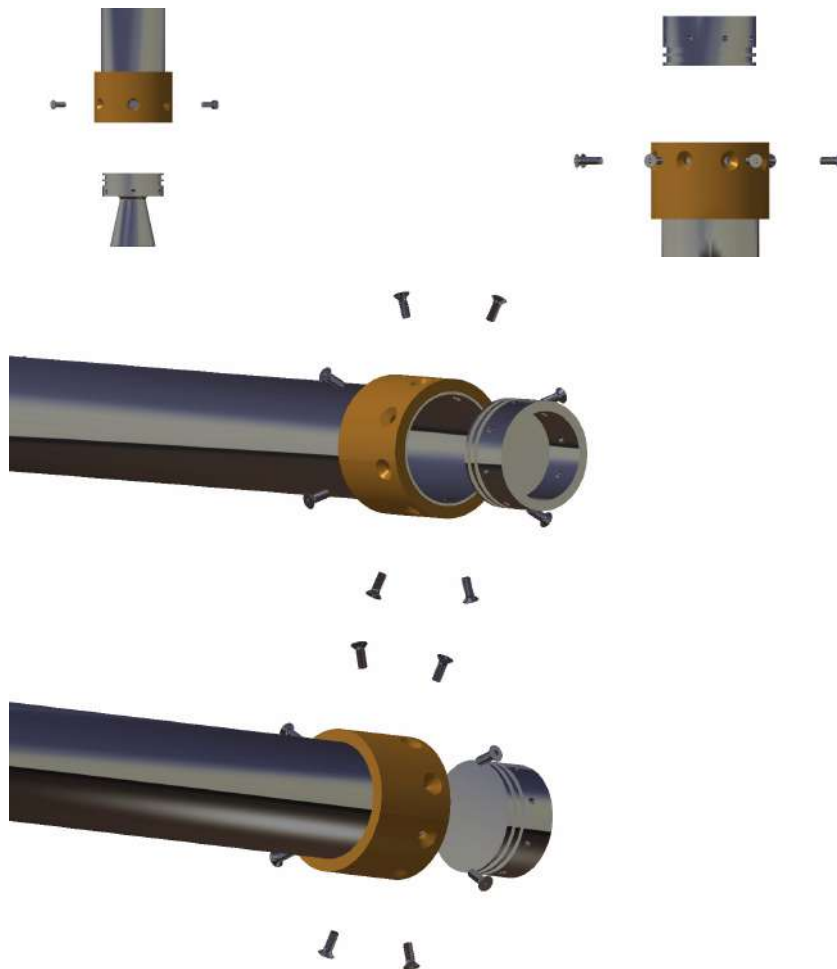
Motor cohete de NAOS vista de ensamblaje .
